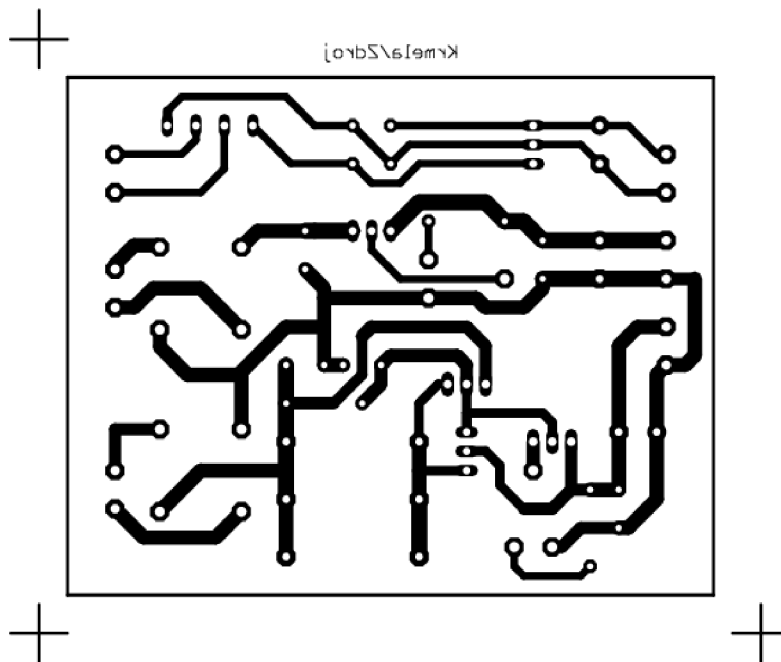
Rozložení součástek na desce plošného spoje M 1:1, rozměr: 62 x 65 mm
